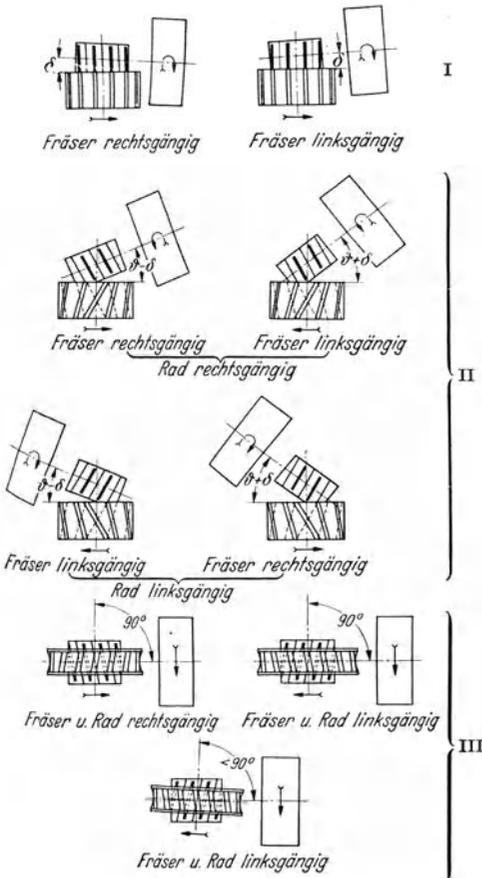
Lage des Fräasers zum Rad beim Fräsen mit Wälzfräser (nach Gläser).
